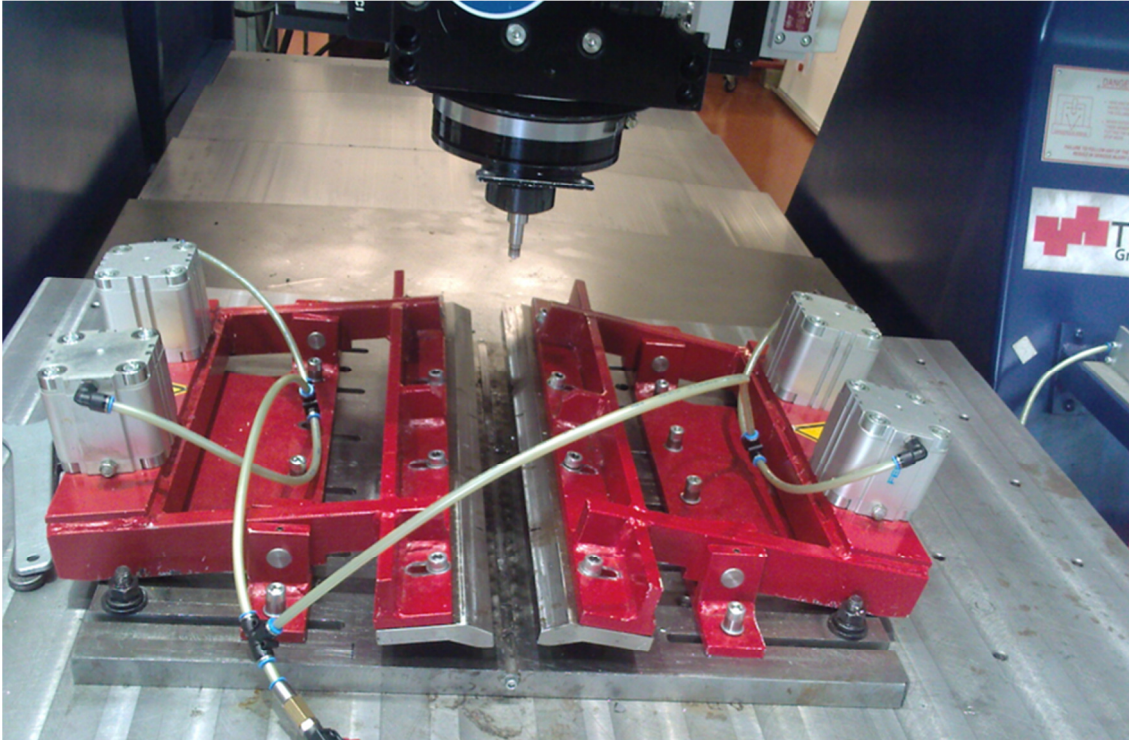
FSW-Anlage MTS ISTIR BR4 - Schweißkopf mit Werkzeug und Spannvorrichtung
